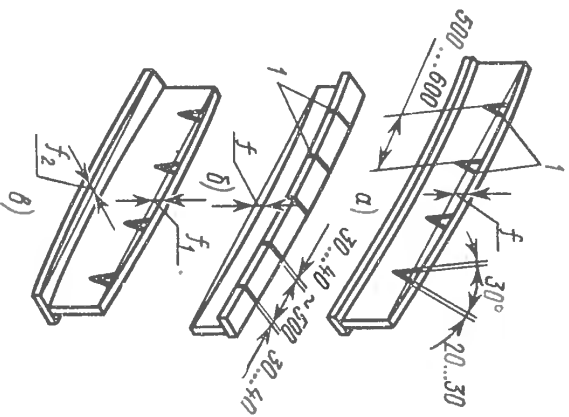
Схемы термической правки балок таврового сечения нагревом верхней части вертикальной стенки (а), нагревом пояса (б) и нагревом вертикальной стенки и пояса (в):
